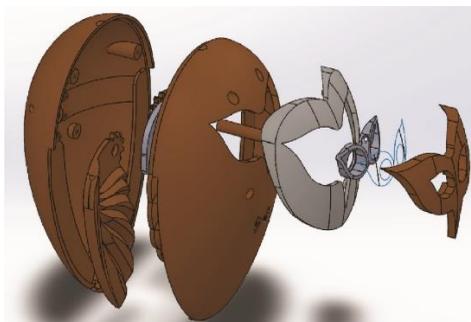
Base engrenagens e motor de passo e pinos fixadores.
